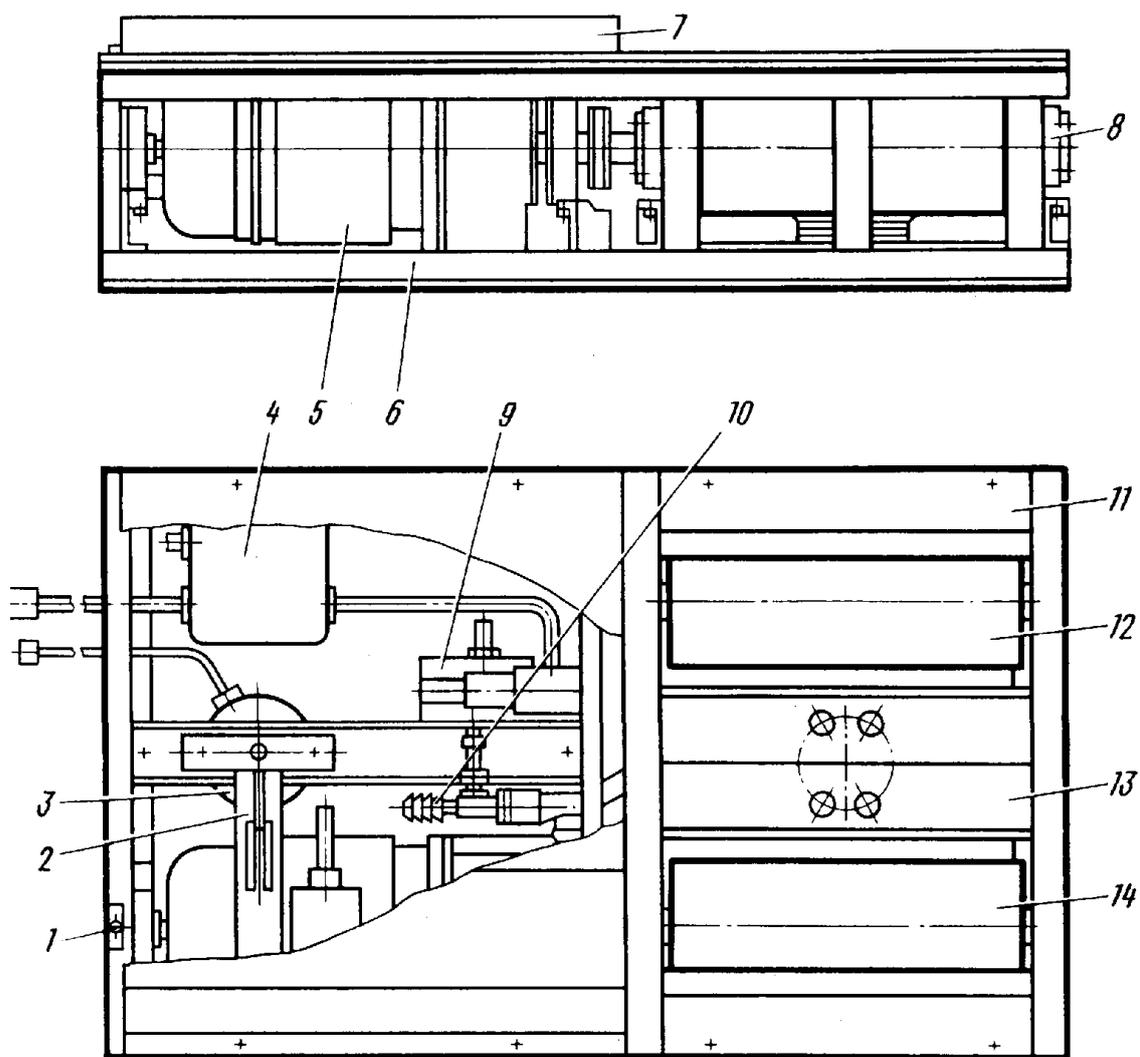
Автоматизированный стенд модели для проверки тормозов
